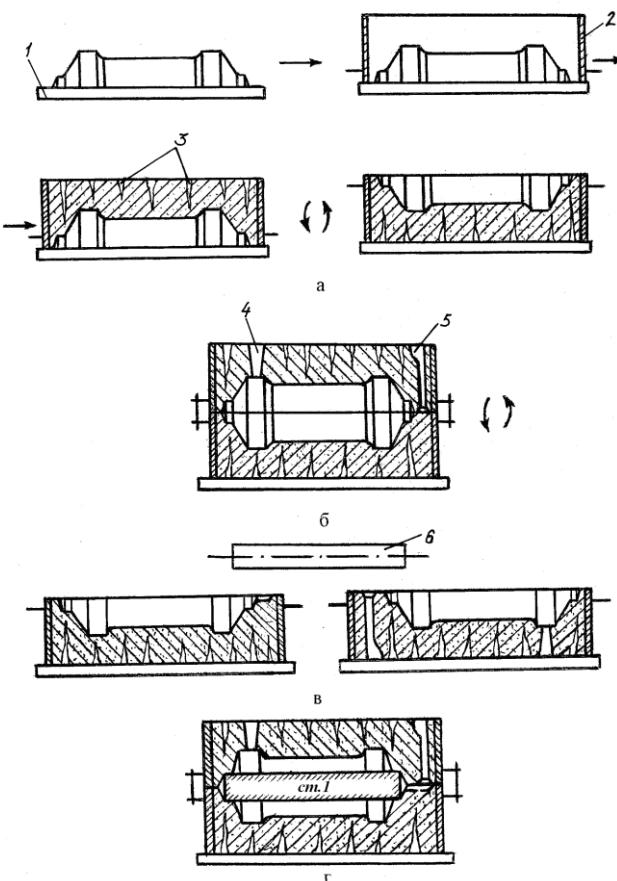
Последовательность изготовления песчано-глинистой формы ручной формовкой в парных опоках по разъемной модели для отливки втулки: а, б – изготовление нижней и верхней полуформ; в – извлечение модели; г – собранная литейная форма (1 – подмодельная доска, 2 – опока, 3 – газоотводящие каналы, 4 – выпор, 5 – литниковая система, 6 – стержень)
